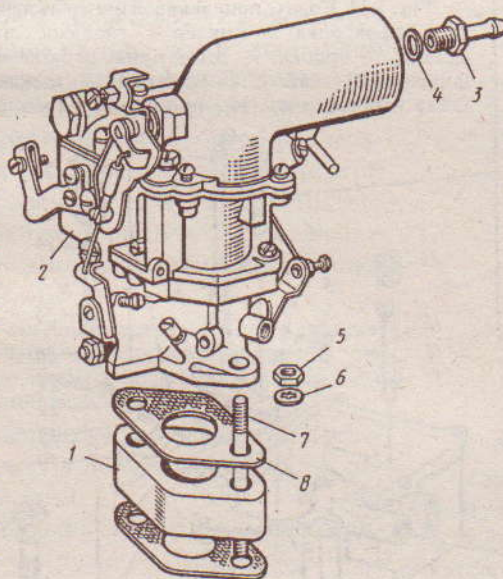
Карбюратор К-127 (по 10.82 г.): 1 - проставка карбюратора; 2 - карбюратор К-127; 3 - штуцер топливоподводящий; 4 - прокладка; 5 - гайка М8; 6 - шайба 8 стопорная; 7 - шпилька крепления карбюратора; 8 - прокладка фланца карбюратора и кронштейна крепления воздушного фильтра
